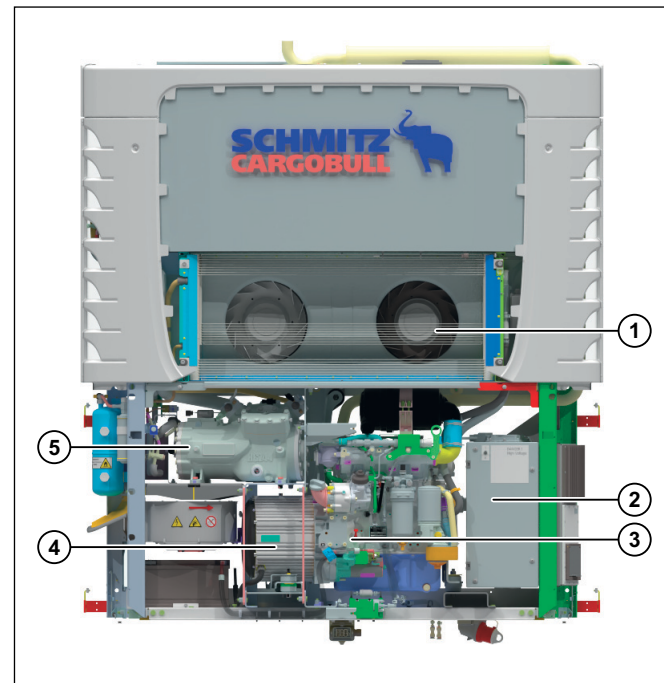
Вид з відчиненими дверима (S.CU dc90)
